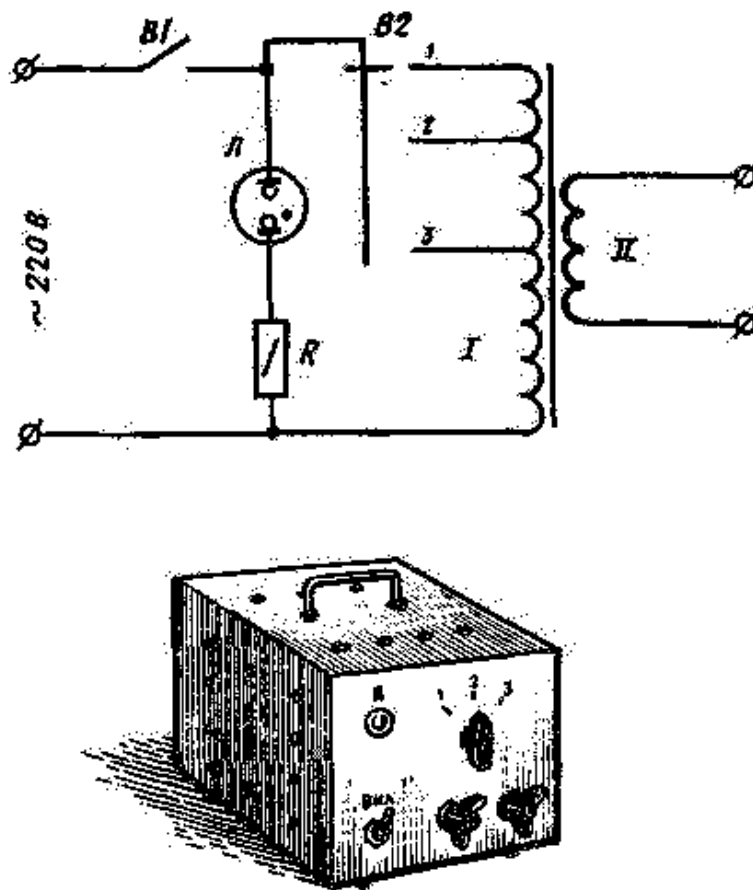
Портативный сварочный аппарат (вторая конструкция)
